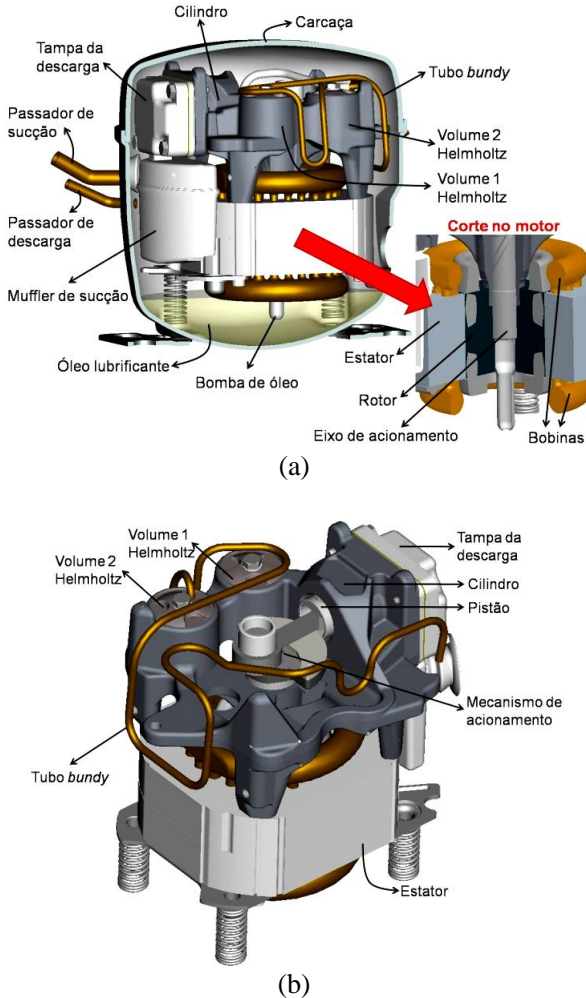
Componentes de um compressor alternativo hermético: (a) Vista do conjunto com a carcaça e detalhe do motor; (b) Vista isolada do mecanismo de compressão.
